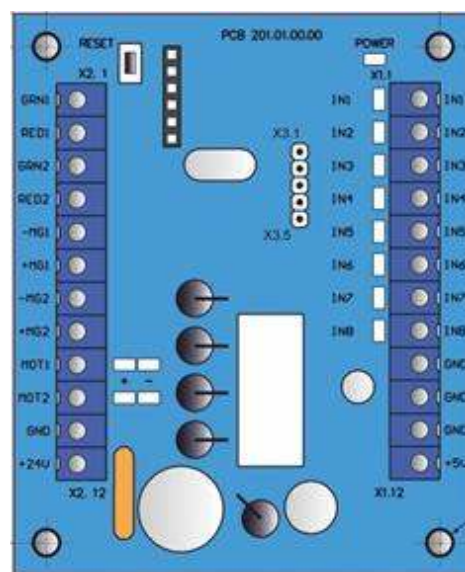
Зовнішній вигляд контролера PCB.201.01.00.00 моторизованого механізму хвіртки
